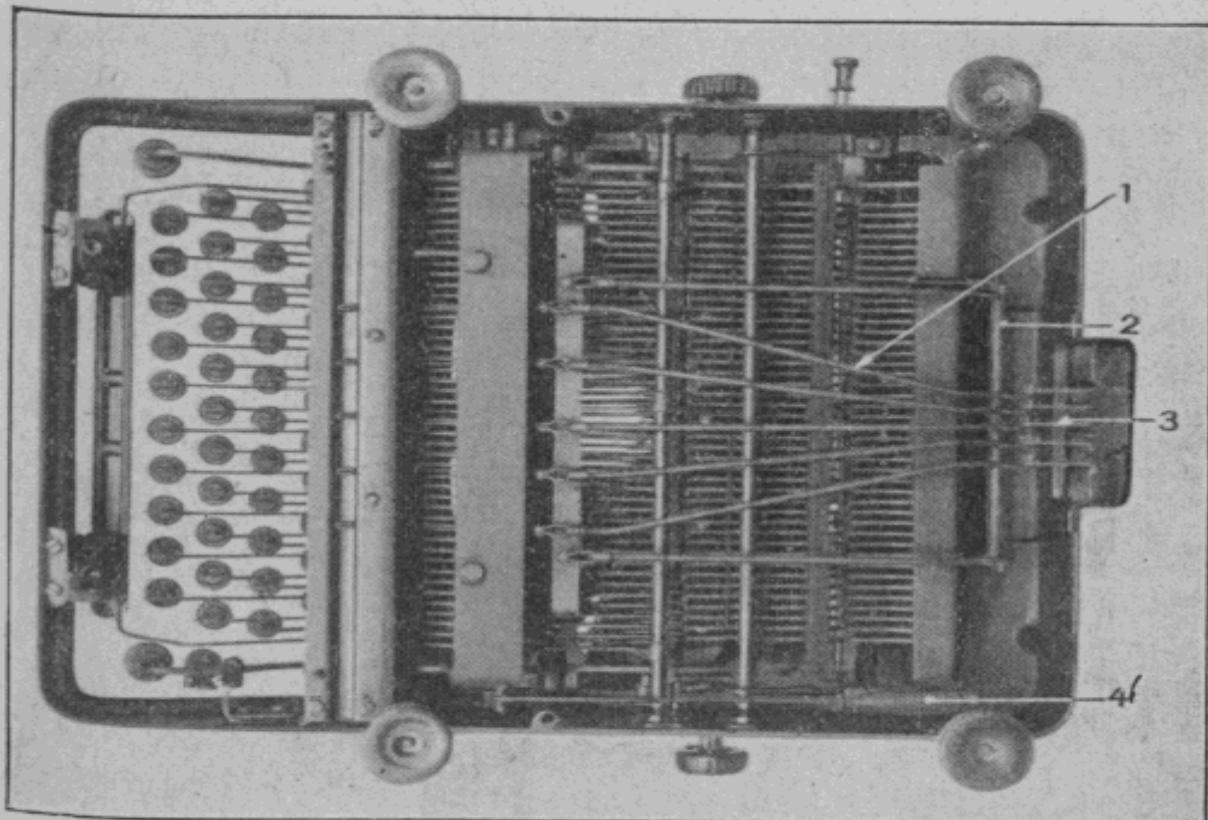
(Type d). Remington 10. Code série à barres plates, vue en dessous.
